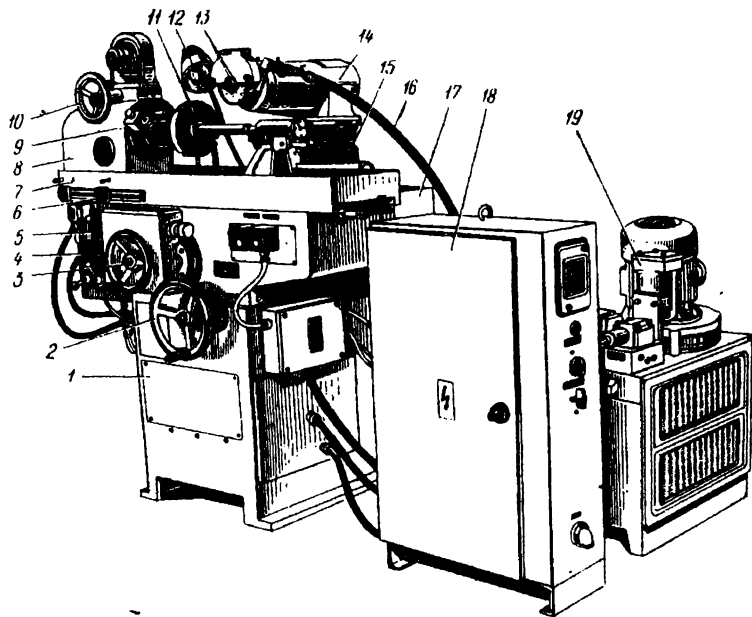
Станок ТчФТ для заточки твердосплавных насадных фрез и ножей
